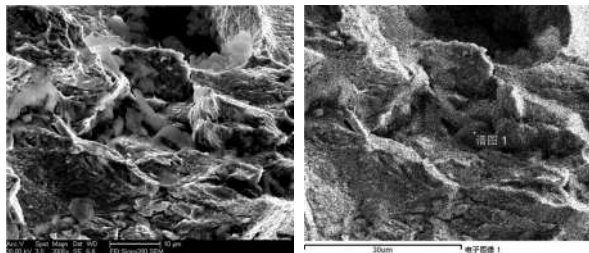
焊管开裂试样裂纹形貌 图4 夹杂物形貌
